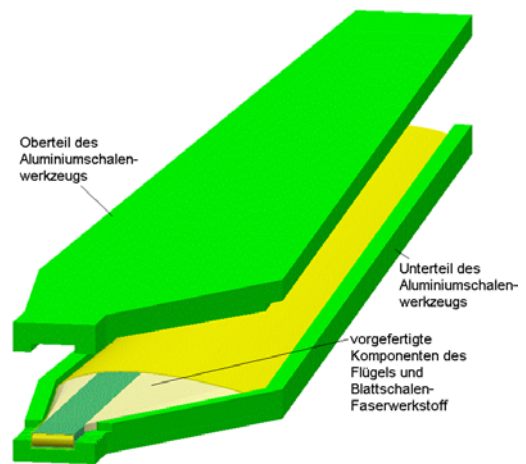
Fertigung des Rotorblattes im Aluminiumschalenwerkzeug
